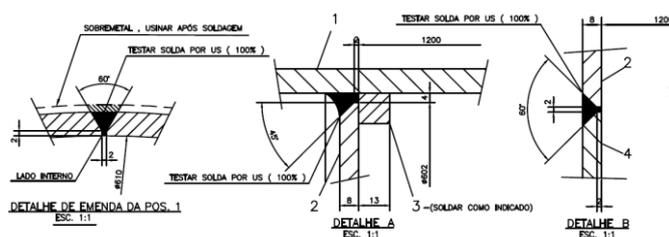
Detalhes de solda, desenho cliente (do Autor, 2020).
